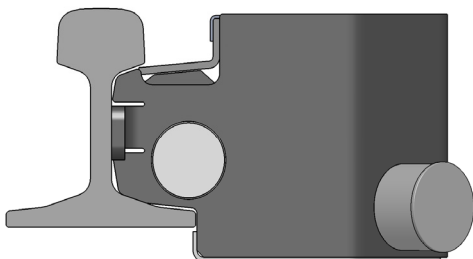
Type SK420-016 (Schienenprofil U50; geschraubt/geschweißt)
